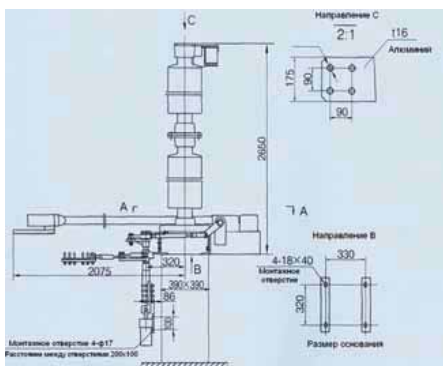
Внешний вид и размеры заземлителя JW -252
